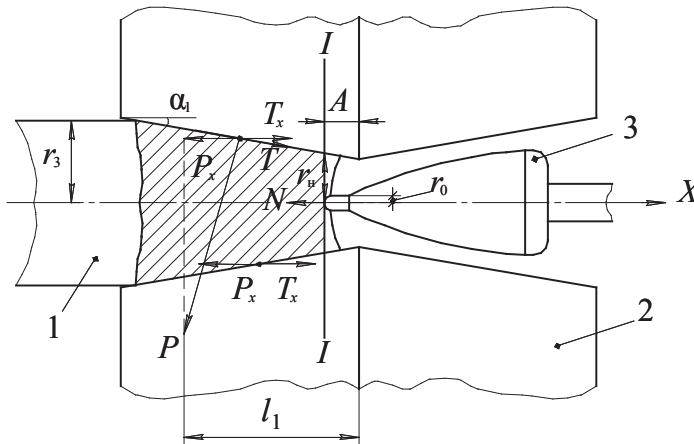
Схема вторичного захвата при винтовой прошивке:
